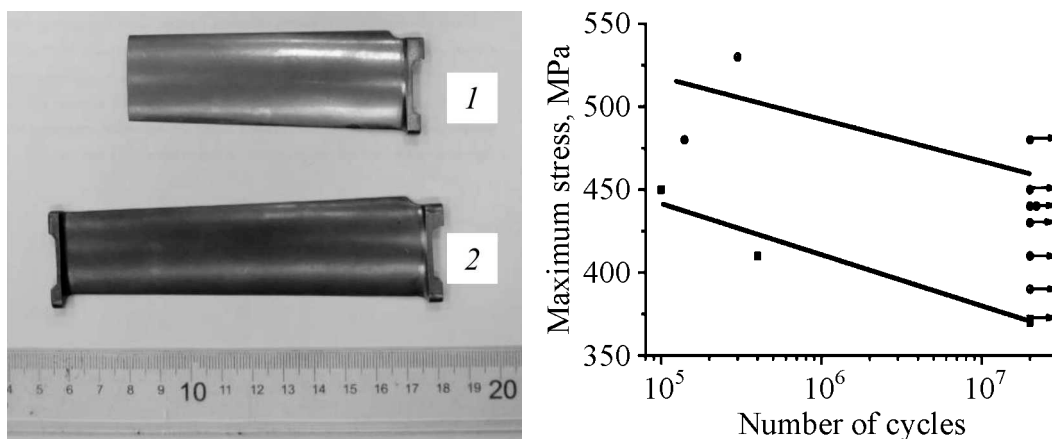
Вид опытной лопатки компрессора низкого давления, полученной из УМЗ-сплава ВТ6 (1), и образца для усталостных испытаний (2)
